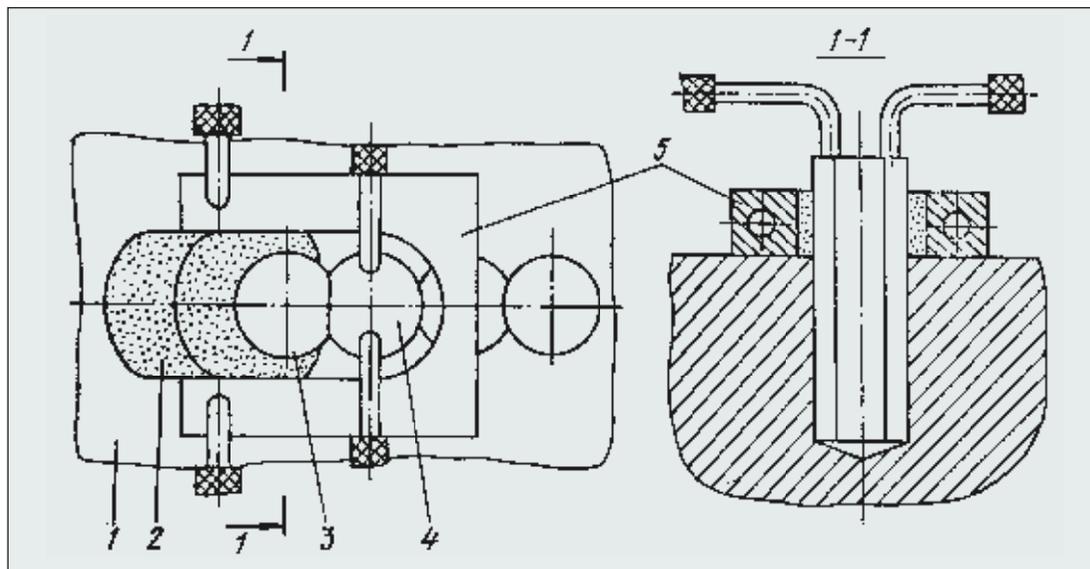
Сварка с водоохлаждаемым кокилем: 1 — изделие; 2 — флюс; 3 — отверстие разделки; 4 — формирующее устройство; 5 — кокиль
